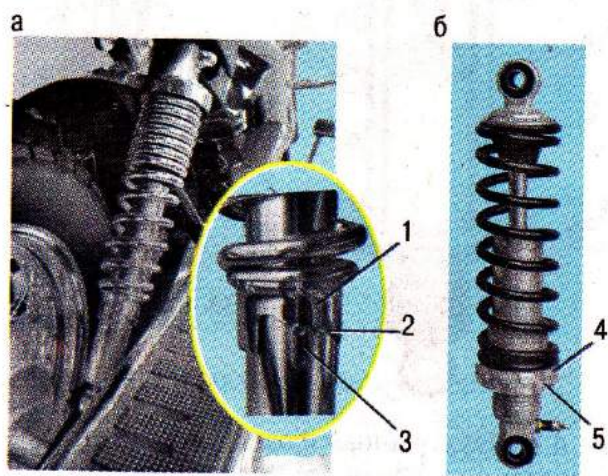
Регулировка преднатяга пружины заднего амортизатора: а – ступенчатая; б – плавная; 1 – нижняя поворотная опора пружины; 2 – канавки; 3 – упор на корпусе амортизатора; 4 – регулировочная гайка; 5 – контргайка
